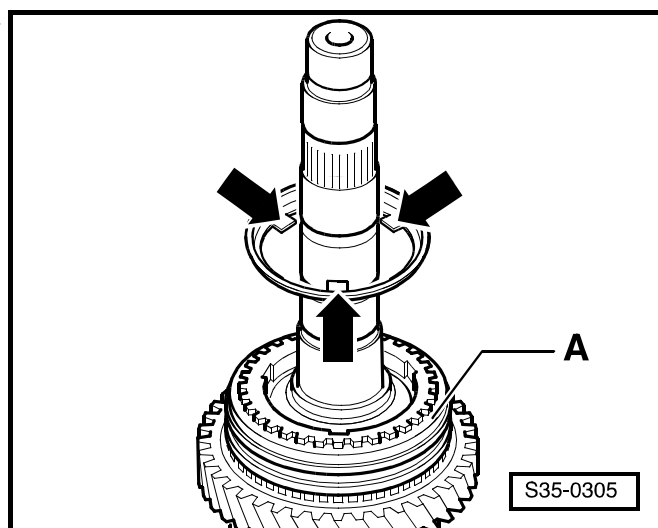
Положение для сборки блокирующего кольца синхронизатора -А- (внутреннего кольца для 1-ой и, соотв., 3. 3-ей передач
